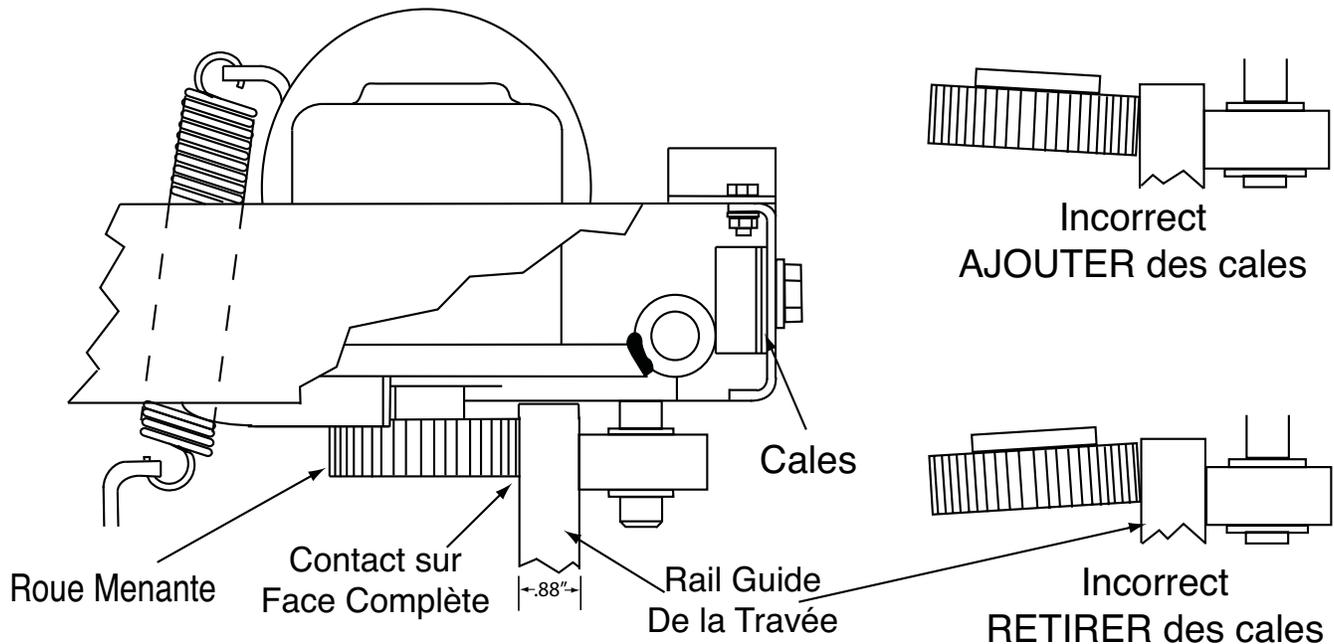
FONCTIONNEMENT SUR PLAN INCLINÉ
